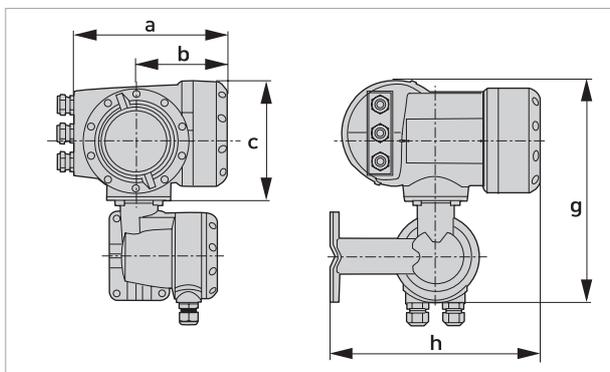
Габаритные размеры прибора в раздельном полевом исполнении (F)
